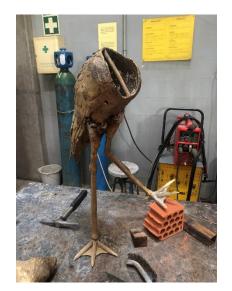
Proceso de soldadura de las patas al torso.
